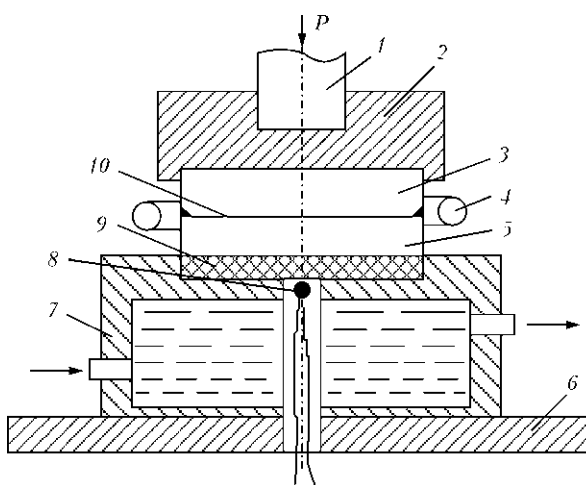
Схема приспособления для пайки АТР: 1 — прижим; 2 — суппорт; 3 — ТД; 4 — индуктор; 5 — АТП; 6 — основа; 7 — холодильник; 8 — термопара; 9 — алмазный слой; 10 — паяный шов
